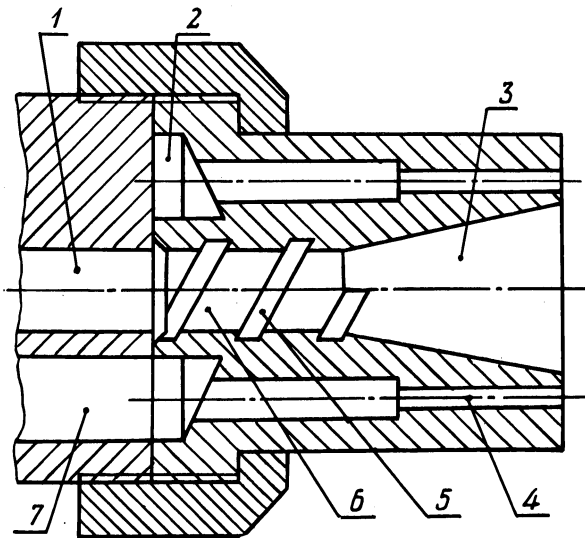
Сопло горелки газопламенного порошкового напыления конструкции БПИ.
